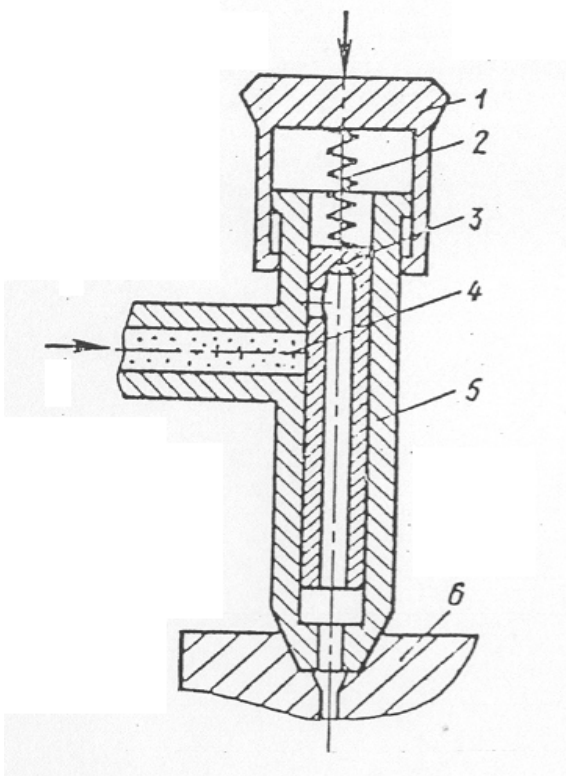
Схема устройства ручного шприца для запрессовки пастообразных модельных составов: 1 – рукоятка; 2 – пружина; 3 – золотник; 4 – модельный состав; 5 – корпус; 6 – пресс-форма.
